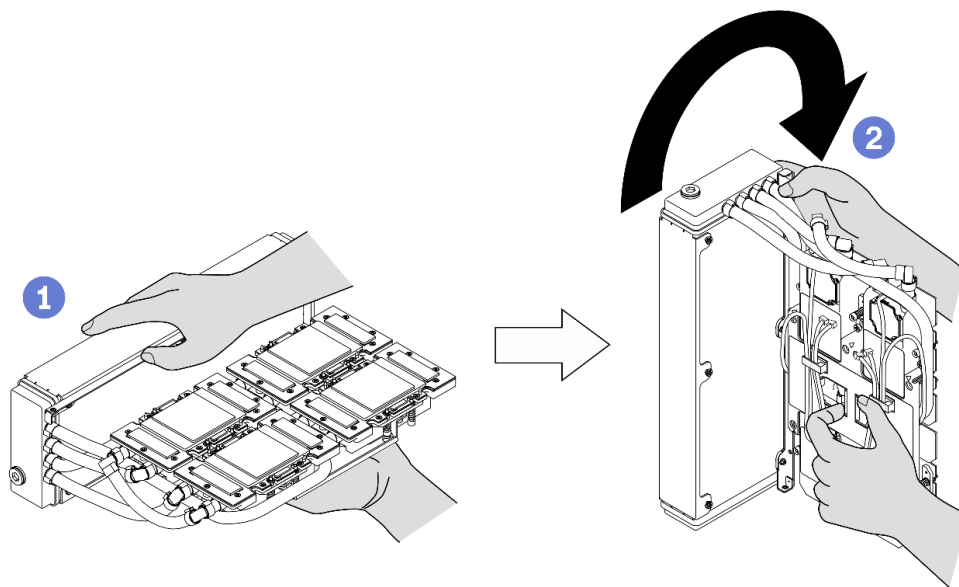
Drehen des L2A im Uhrzeigersinn
